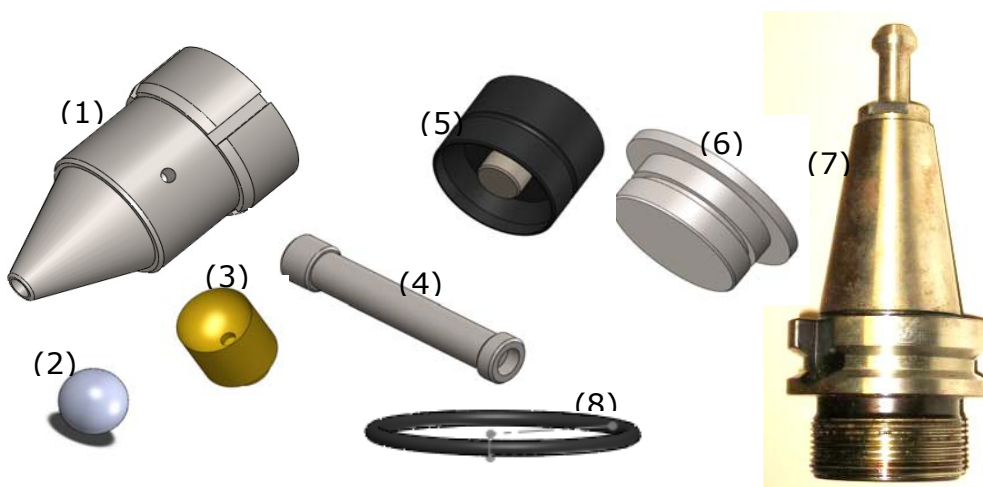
(1) Cuerpo principal de la herramienta, (2) Bola de diámetro 10mm, (3) Casquillo de fricción, (4) Vástago o guiador, (5) Taqué hidráulico, (6) Tapa superior del cuerpo, (7) Cono BT-40 utilizado para el acoplamiento a la máquina, (8) Junta tórica.
